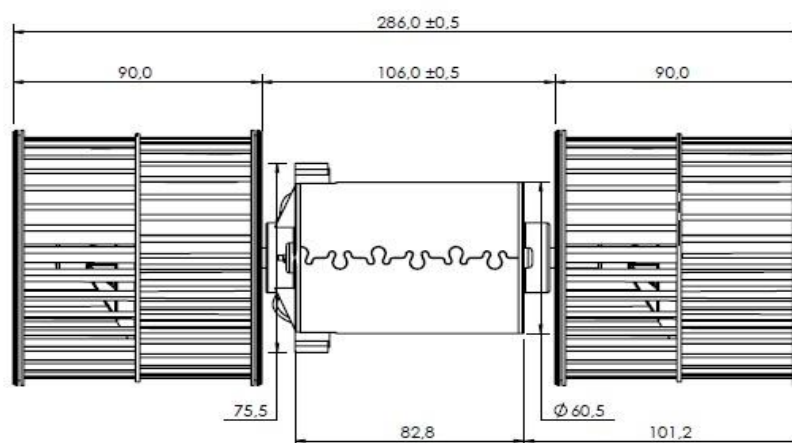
17 Desenho técnico eletroventilador, Imobras 24V, CC.
